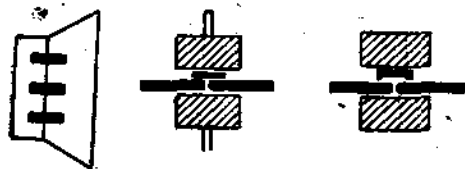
Законченная сварка и правильный и неправильный способы ее исполнения при сварке мостиком.
